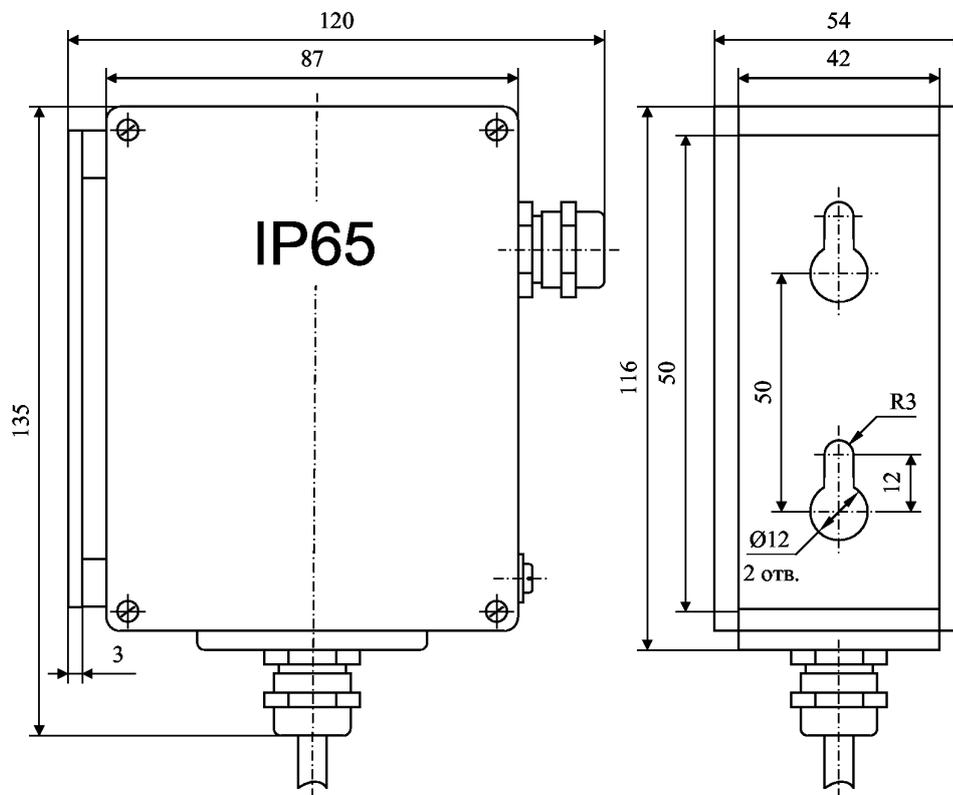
Корпус ПП для навесного монтажа
